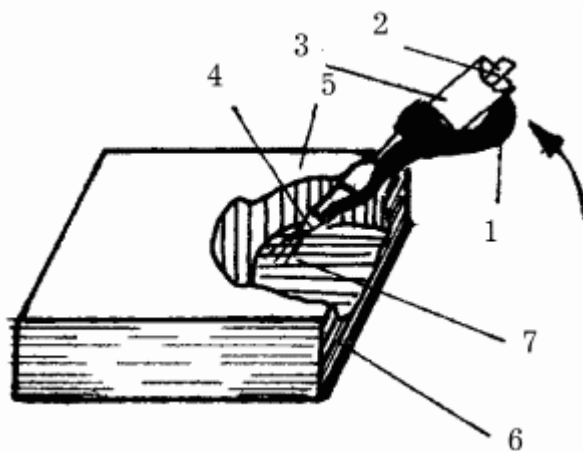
Резак для воздушно-дуговой резки: 1 – трубка подачи воздуха; 2 – подача электродной проволоки; 3 – корпус резака; 4 – дуга; 5 – сопло подачи сжатого воздуха в зону горения; 6 – заготовка; 7 – выплавленный участок заготовки.
